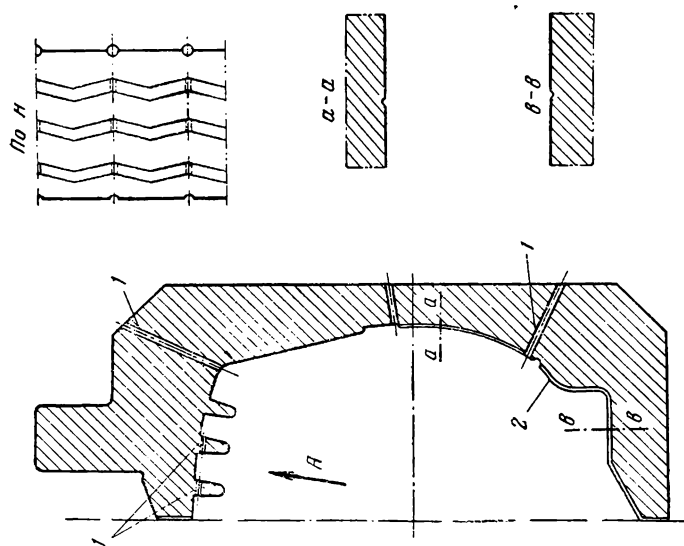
Сверления (1) и риски (2) по формующей поверхности прессформы.
